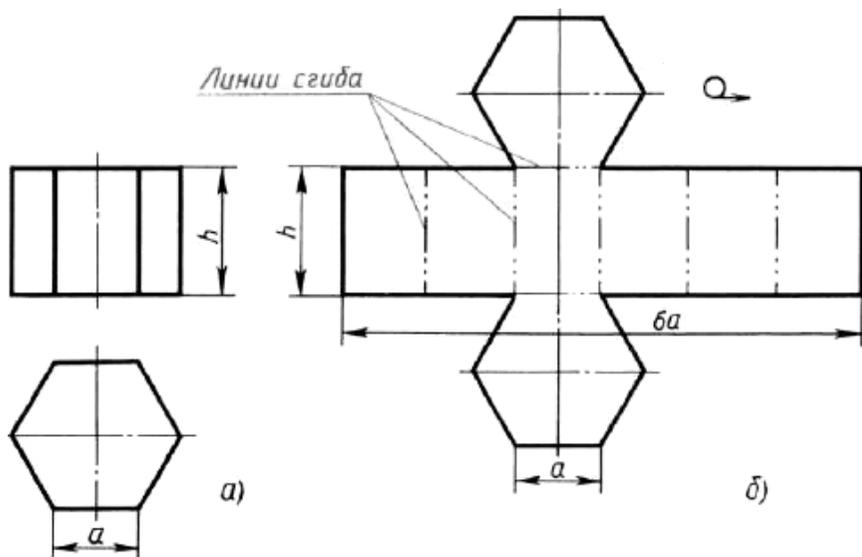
Построение чертежа развертки с основанием шестиугольной призмы: а – два вида; б – развертка поверхностей.
